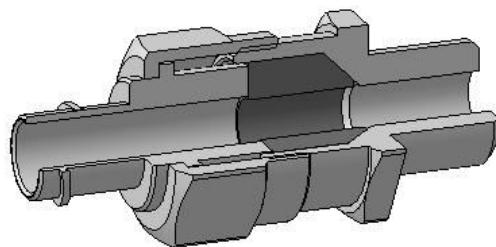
Конструкция кабельного ввода ВН с фитингом для монтажа кабеля в трубе
